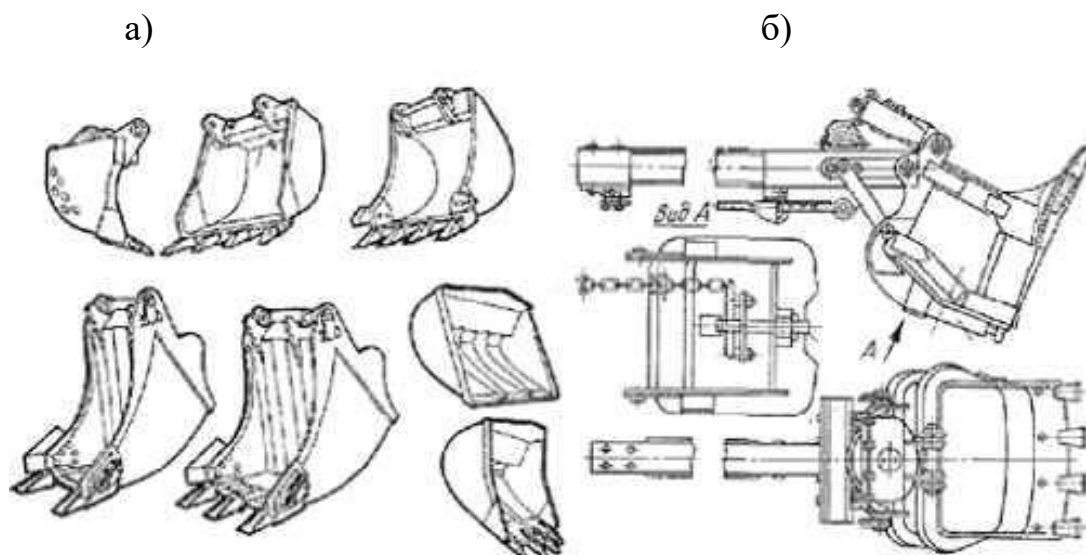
Ковши: а) - обратной лопаты; б - прямой лопаты
